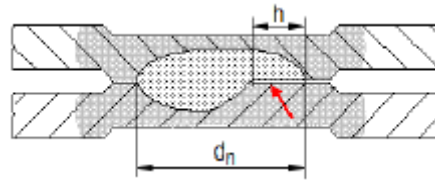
Representação de falta de fusão no ponto de soldadura
